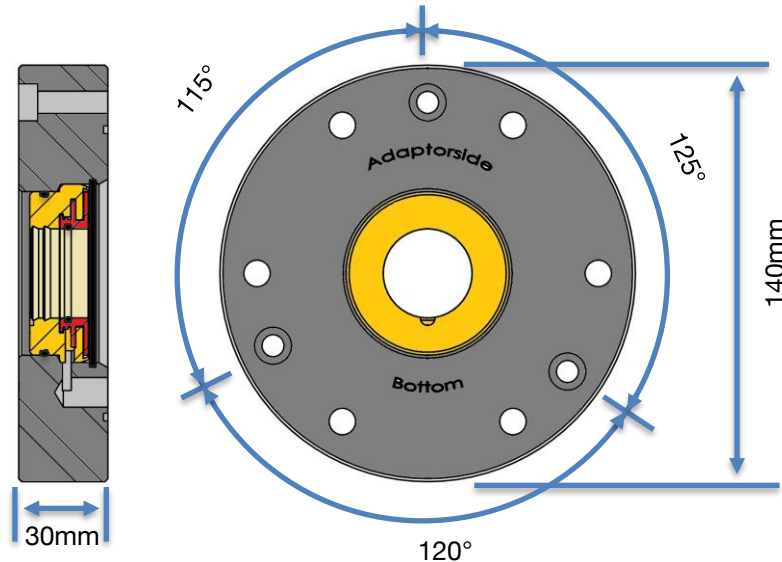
Wellen Dichtsystem BEAROMOS®
